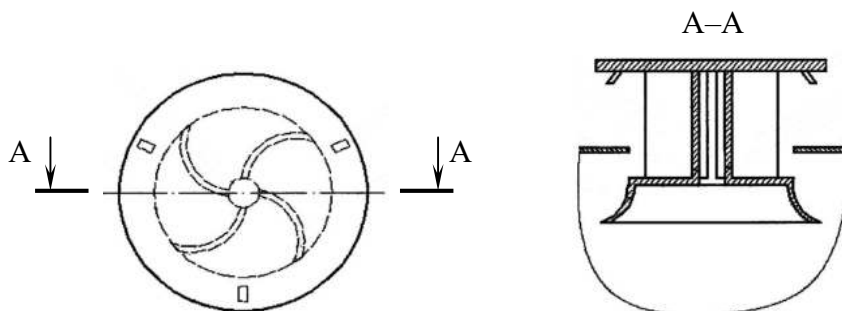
Обертовий клапан згідно з пат. № CN203342819U
